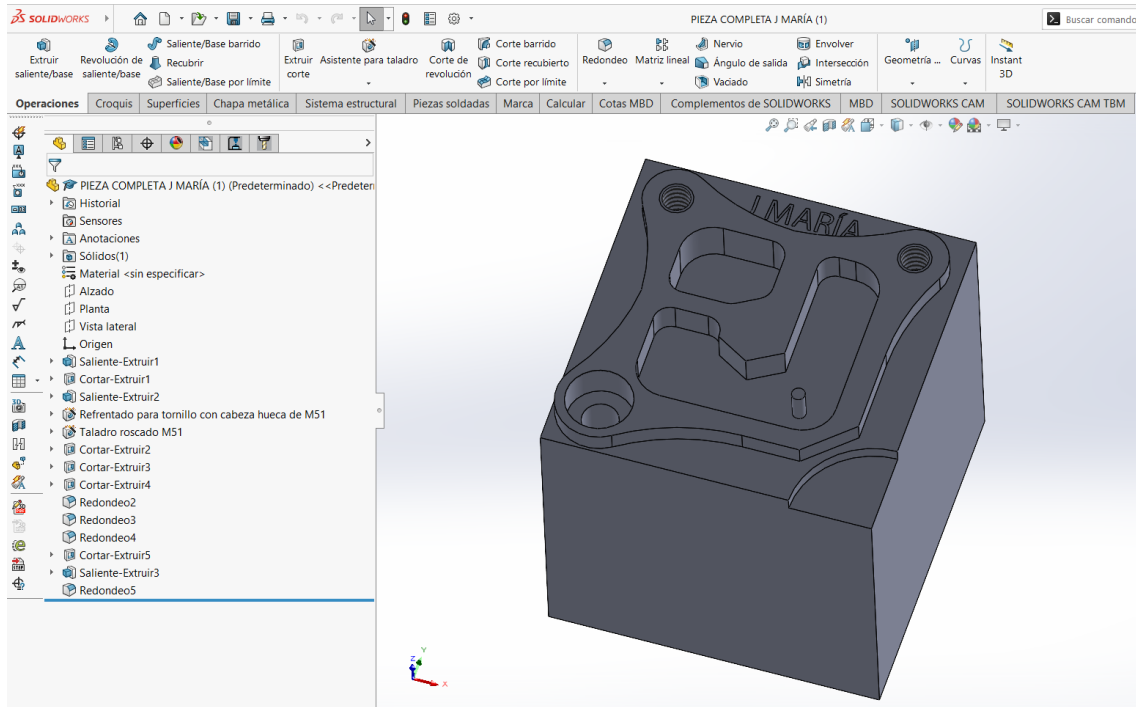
Diseño del ensayo de tolerancias geométricas y dimensionales
